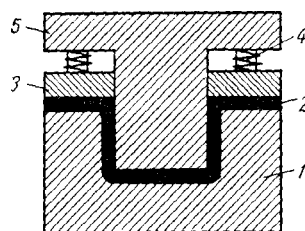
Гидравлический пресс для переработки пластмасс методом горячего штампования: 1 – матрица; 2 – заготовка; 3 – прижимная плита; 4 – пружина; 5 – пуансон
